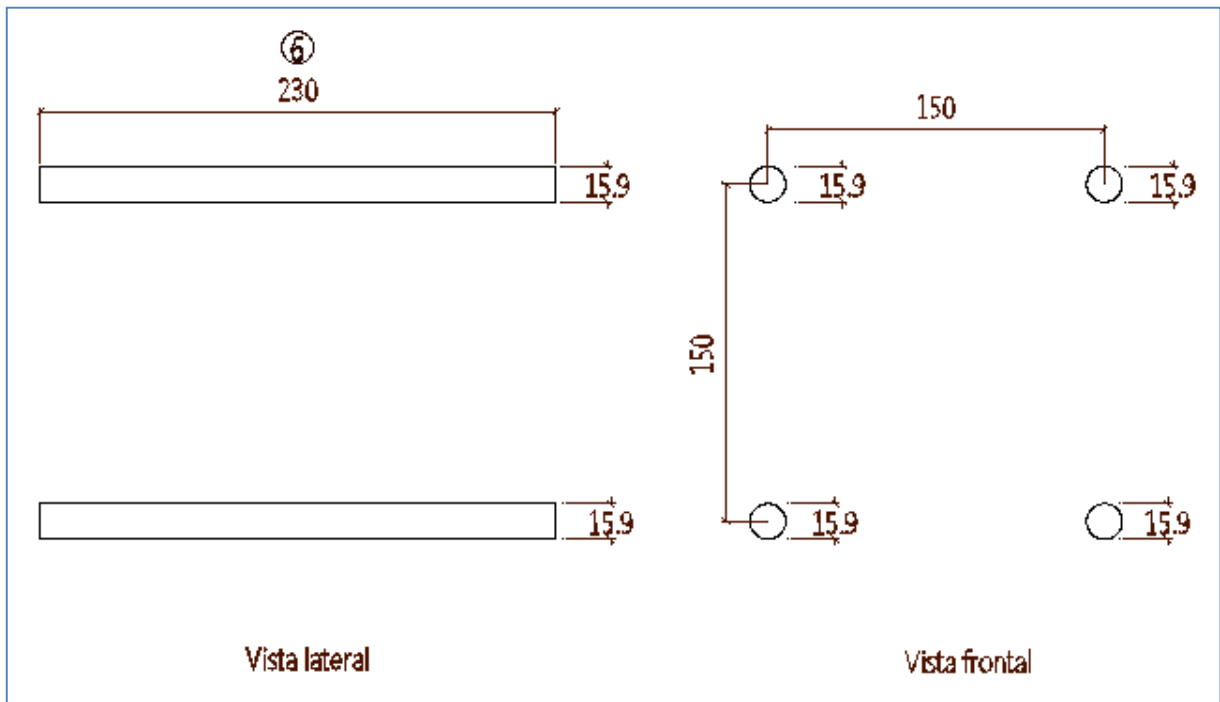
Detalle despiece pieza No.6 modelo 1 tensión.
